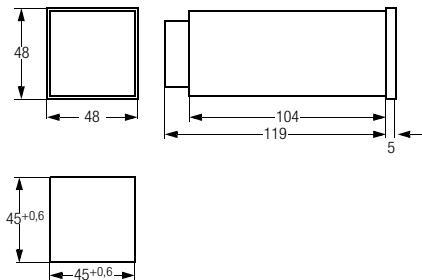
, Gehäuseabmessungen und Schalttafel Ausschnitt
